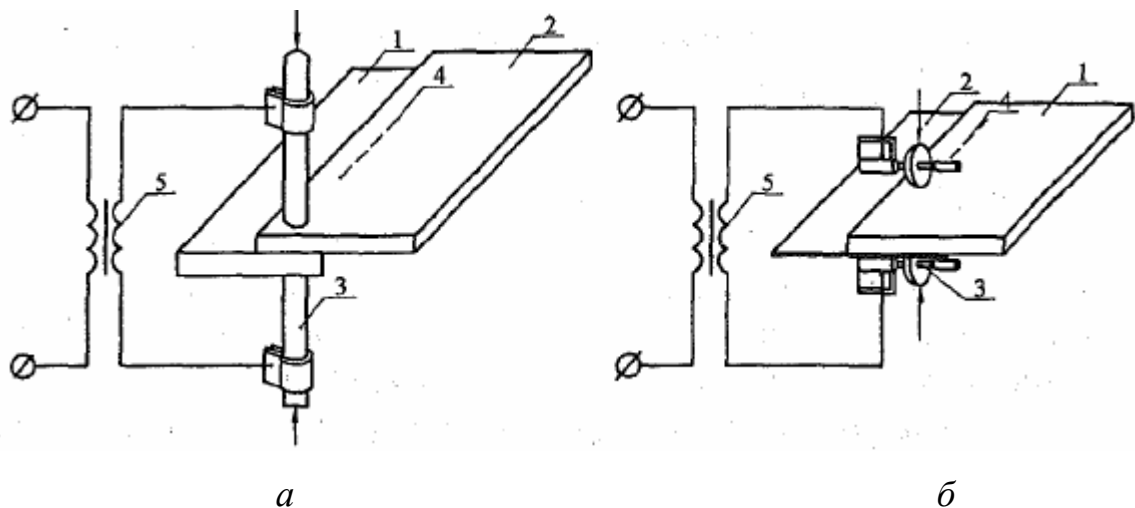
Схеми контактної зварювання: *а* – точкового; *б* – шовного; 1,2 – зварювані елементи; 3 – електроди; 4 – зварні точки (зварний шов); 5 – трансформатор
